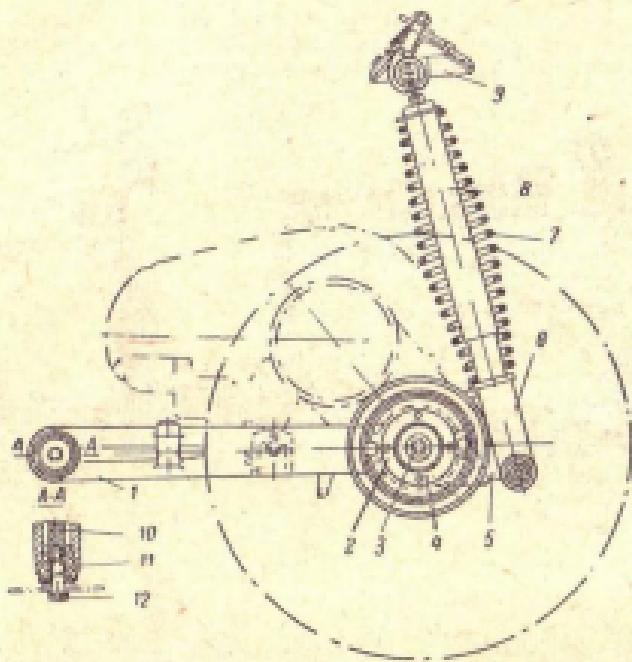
Подвеска заднего колеса мотороллера ВП-150:
